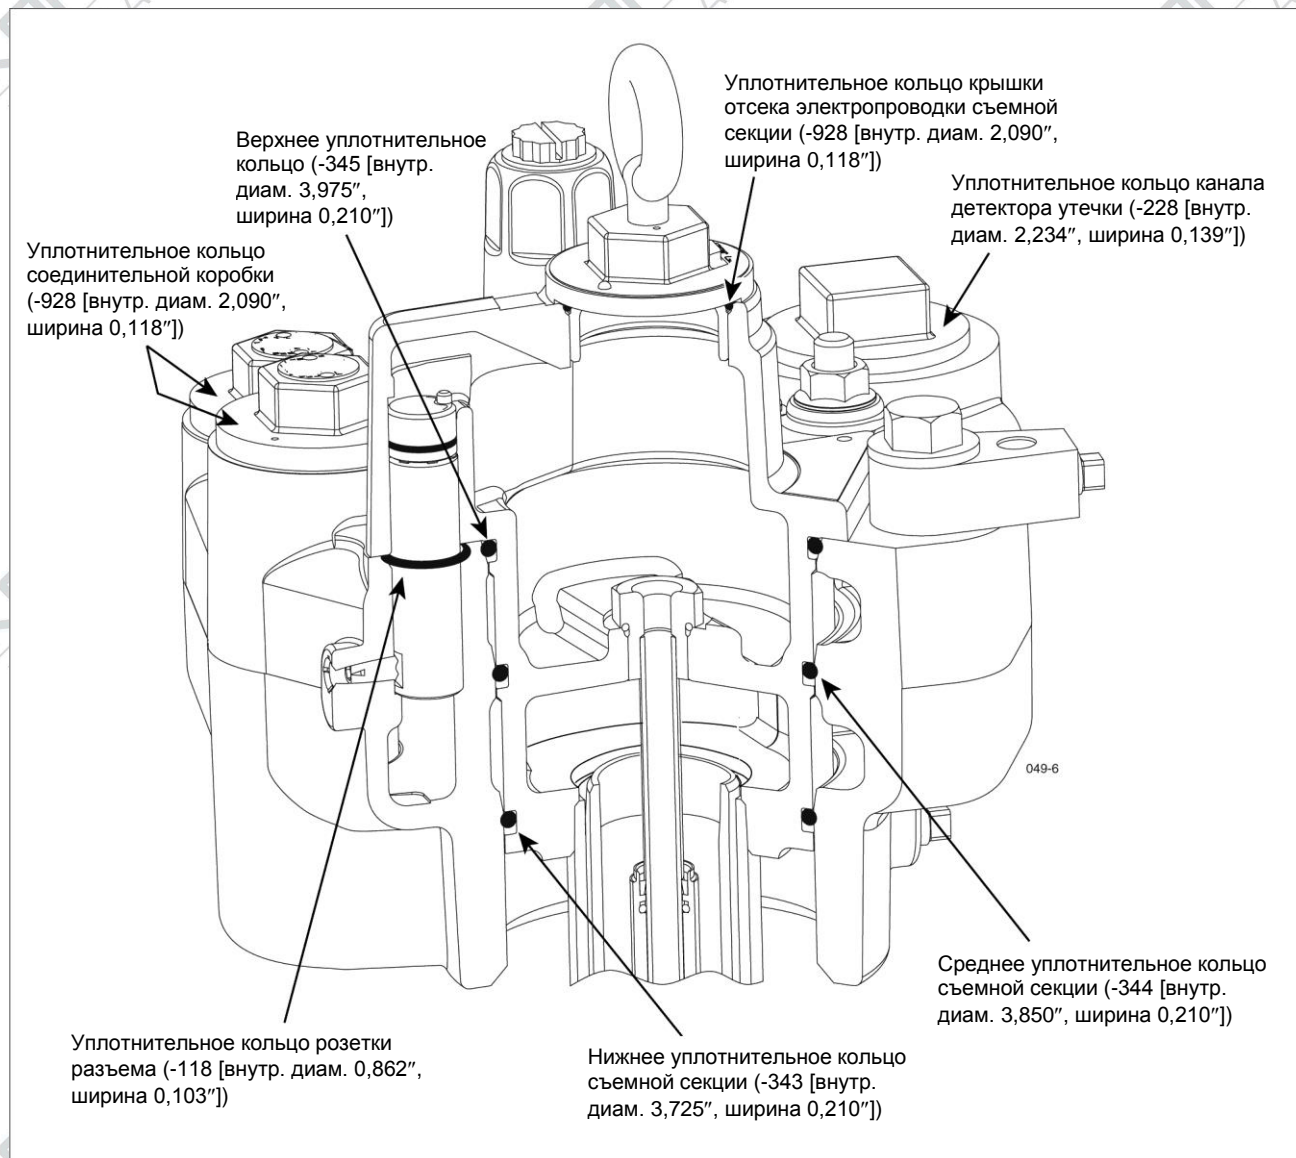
Местоположения уплотнительных колец пакера и манифольда
